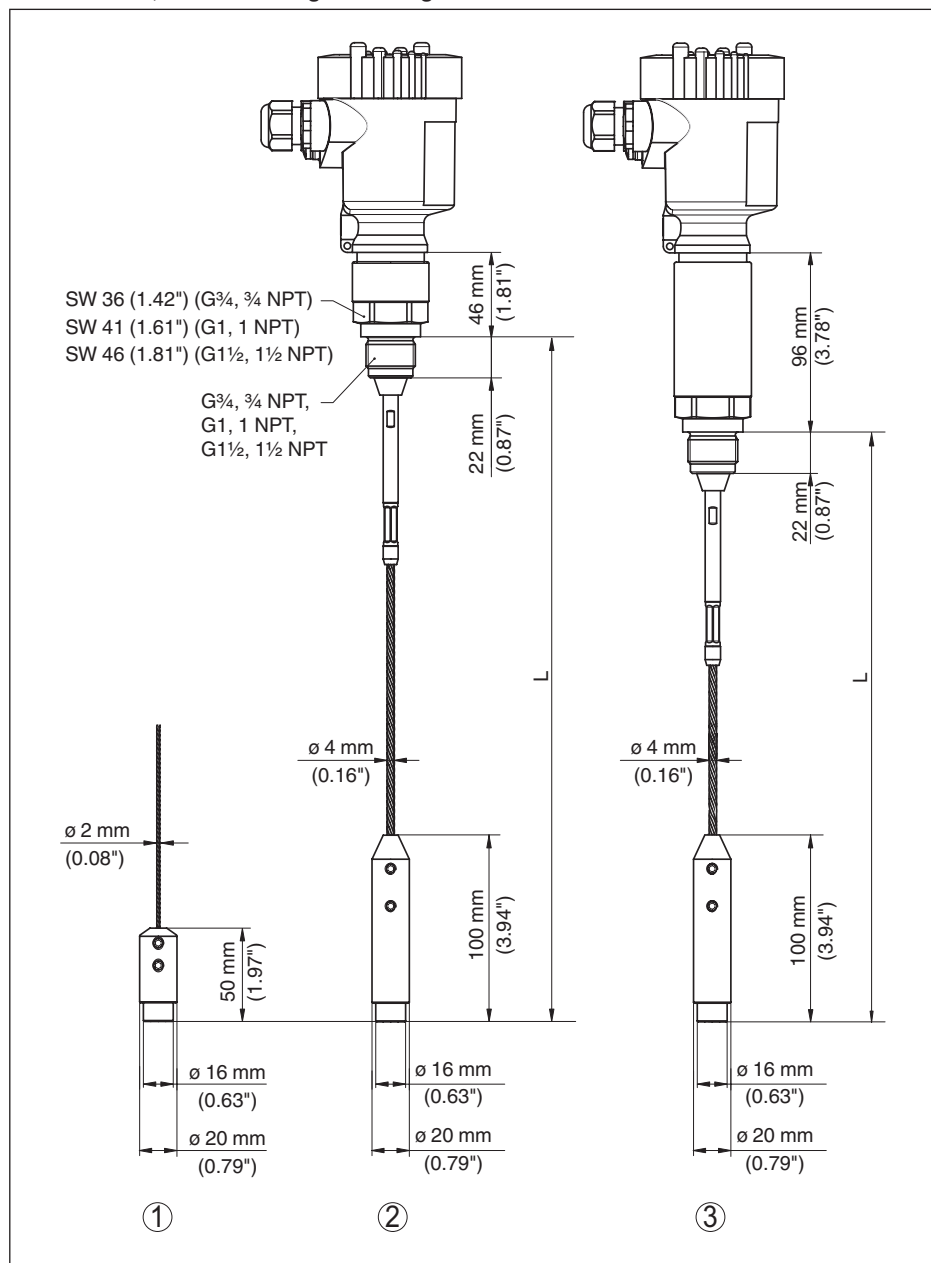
VEGAFLEX 81, Gewindeausführung mit Straffgewicht (alle Straffgewichte mit Gewinde M8 für Ringschraube)
